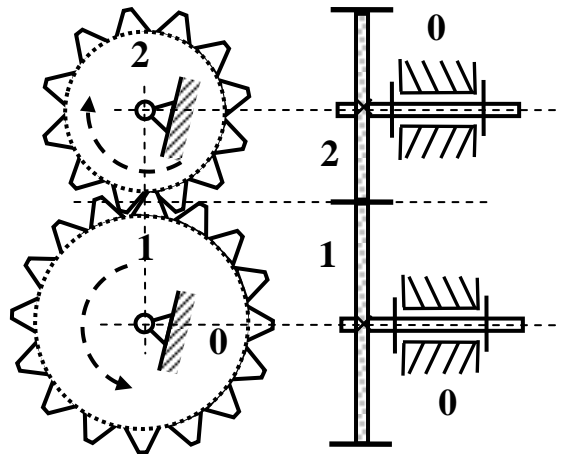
Зубчатый механизм с колесами 1, 2 и стойкой 0
